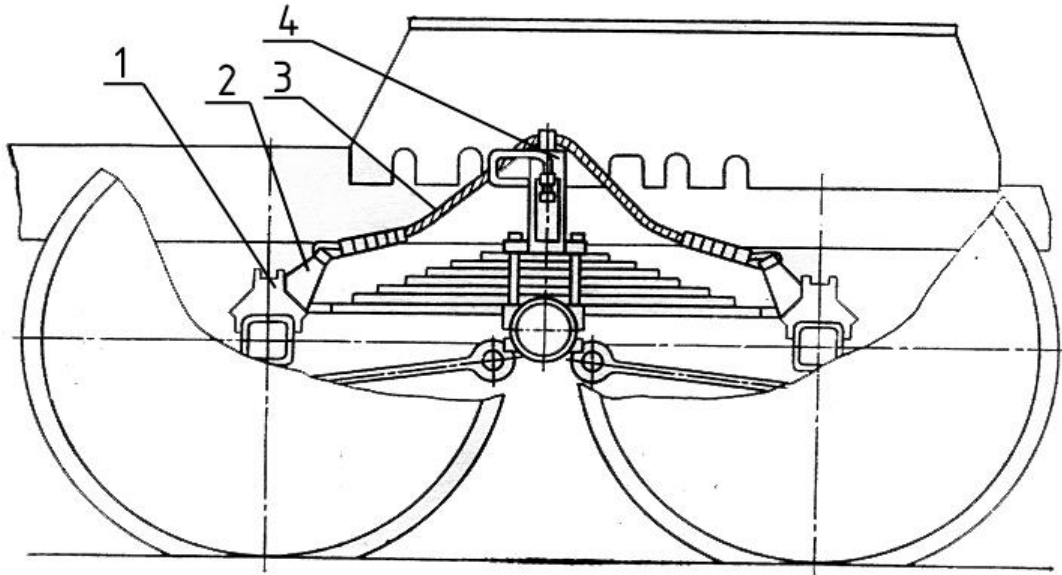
Механизм блокировки рессор двух задних осей автомобиля: 1 кронштейн, 2 серьга, 3 стальной канат, 4 гидроцилиндр.
